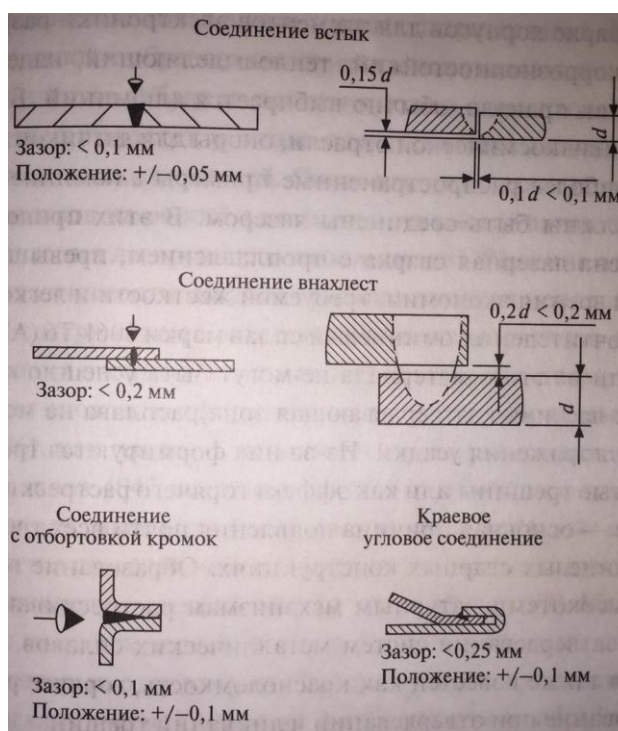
Максимальный зазор и позиционные допуски для разных сварных соединений
